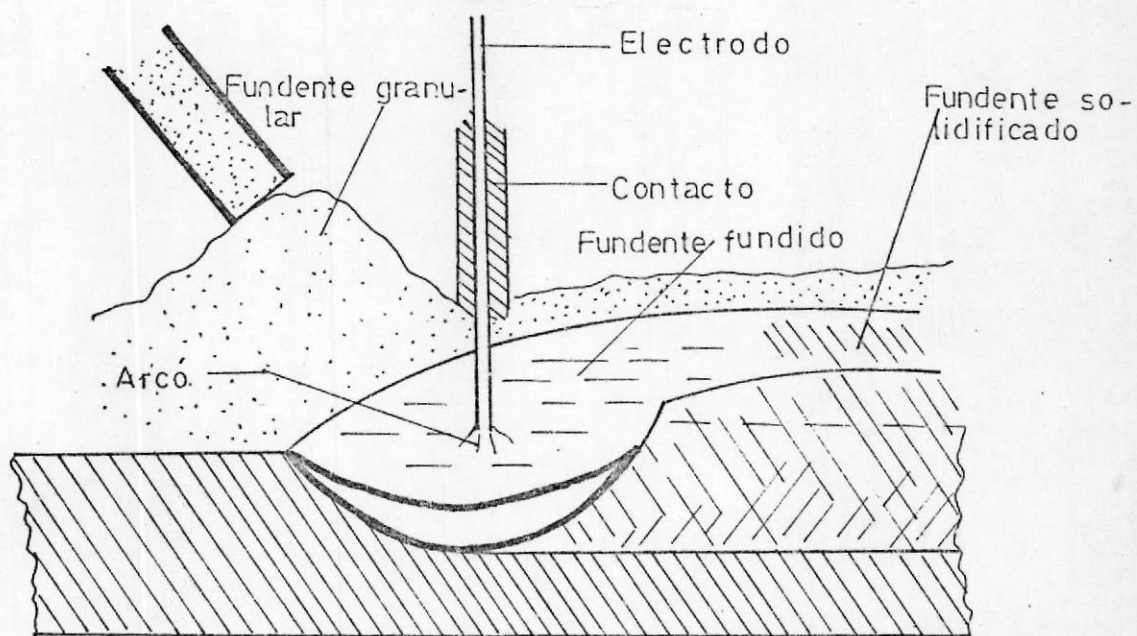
PROCESO DE SOLDADURA AL ARCO SUMERGIDO (6).
